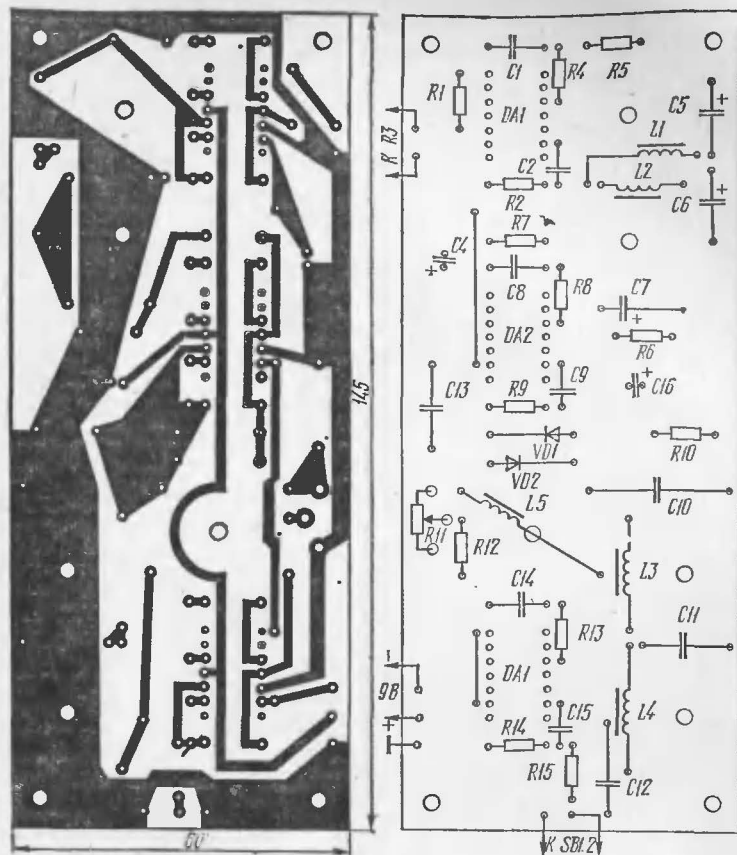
Печатная плата компрессора и схема соединения деталей на ней
